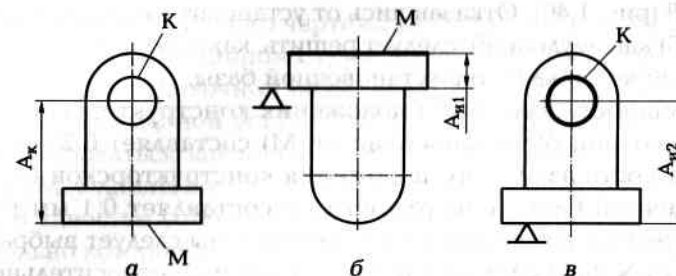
Последовательность обработки поверхностей: а — чертеж конструктора; б — обработка плоскости; в — обработка отверстия
